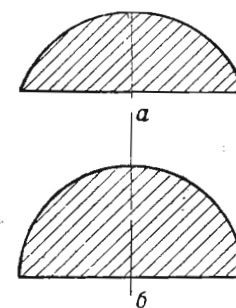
Профили, калибровка которых аналогична калибровке полосовой стали:
